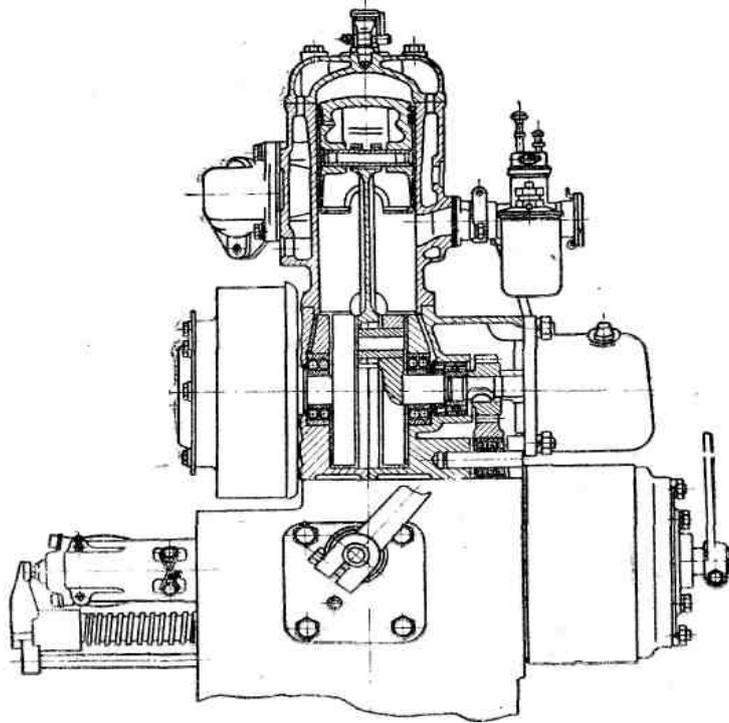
Пусковой двигатель дизеля [КД-35](#)
